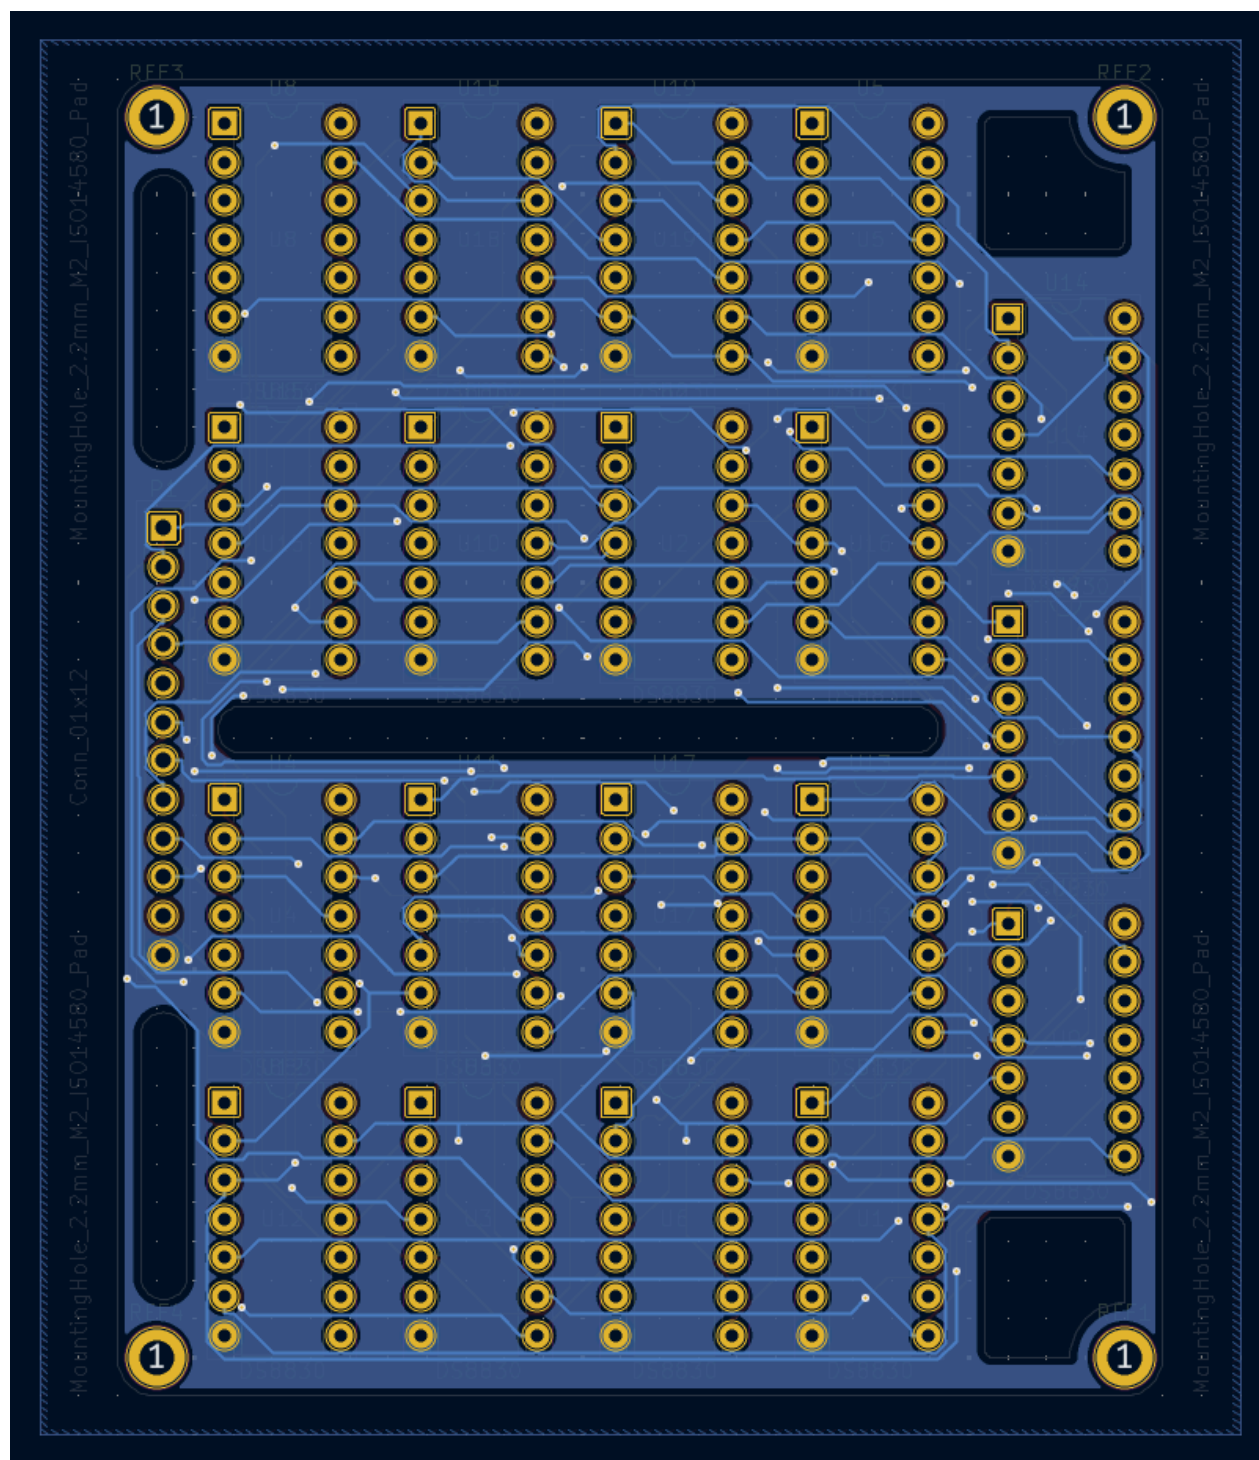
Нижний слой (B.Cu - Back) печатной платы
